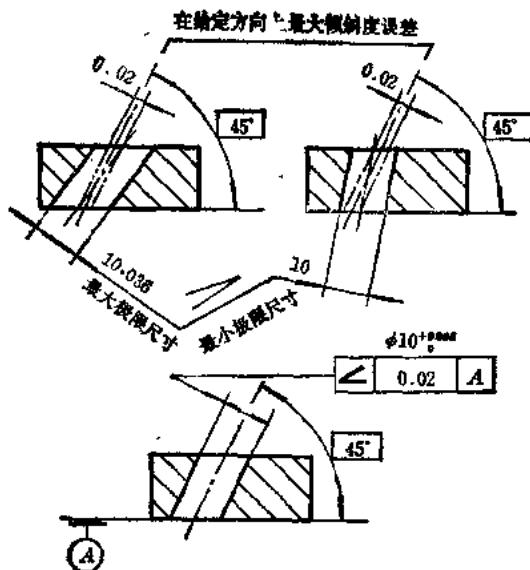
采用独立原则的板孔倾斜度公差与尺寸公差无关
